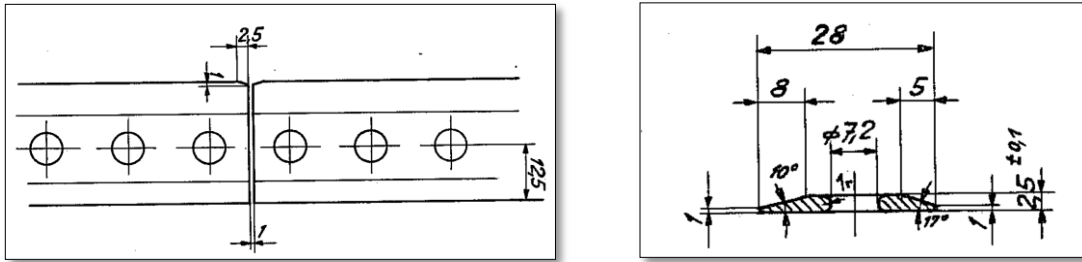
dimensioni del bendaggio del 1° stadio della macchina n° 3.
